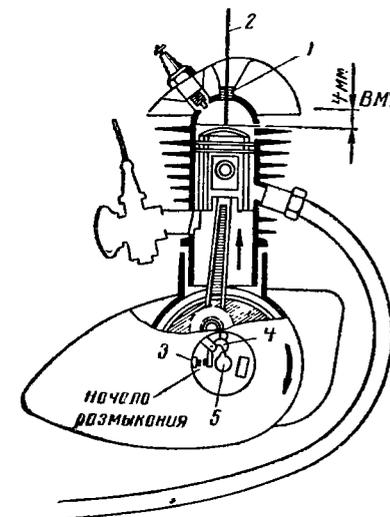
Схема установки зажигания: 1—отверстие для декомпрессора; 2—стержень для определения в. м. т.; 3—неподвижный контакт прерывателя; 4—рычажок прерывателя; 5—кулачок.
